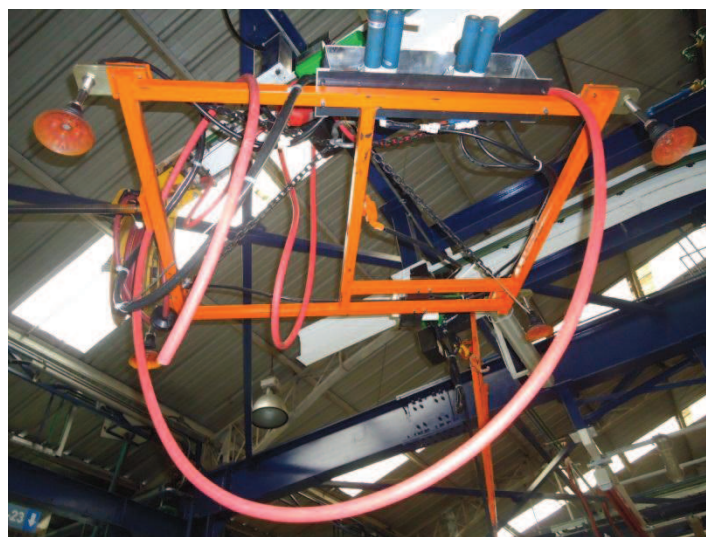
Dispositivo Elevación y Traslado de Techos
